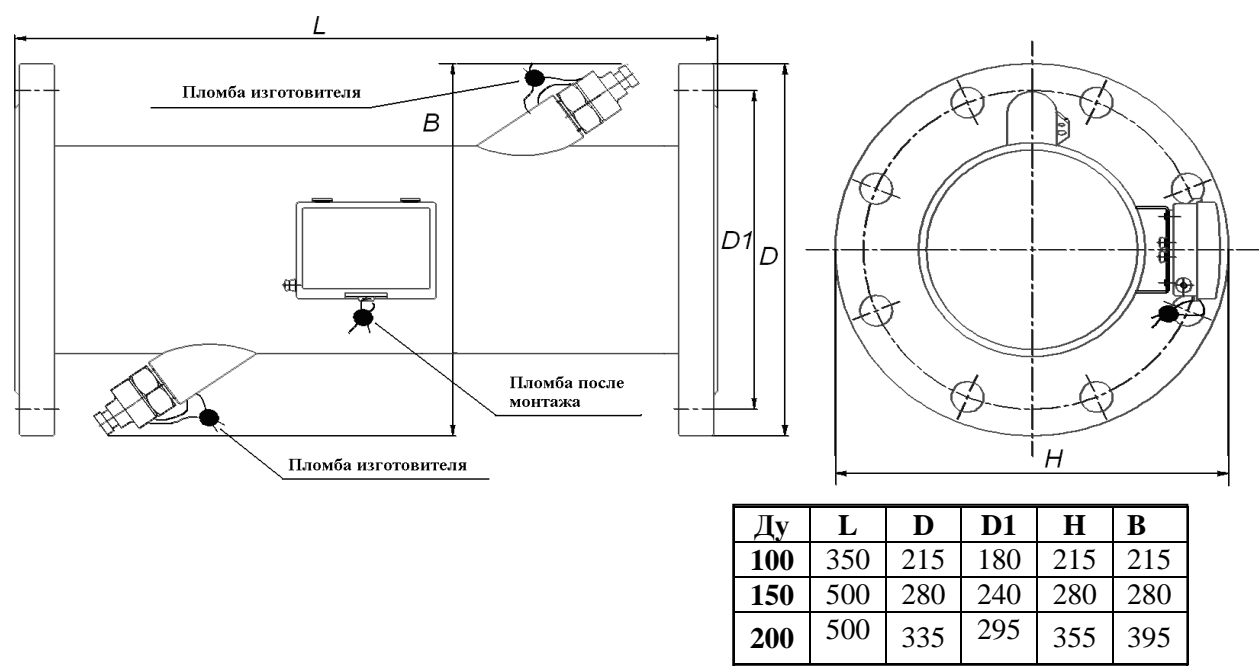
Габаритные размеры ультразвукового преобразователя расхода с Ду100, Ду150, Ду200 (Стальной корпус)
